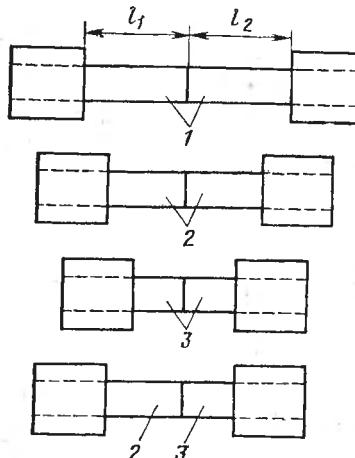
Установочная длина деталей  $l_1 + l_2$  при стыковой сварке сопротивлением:
